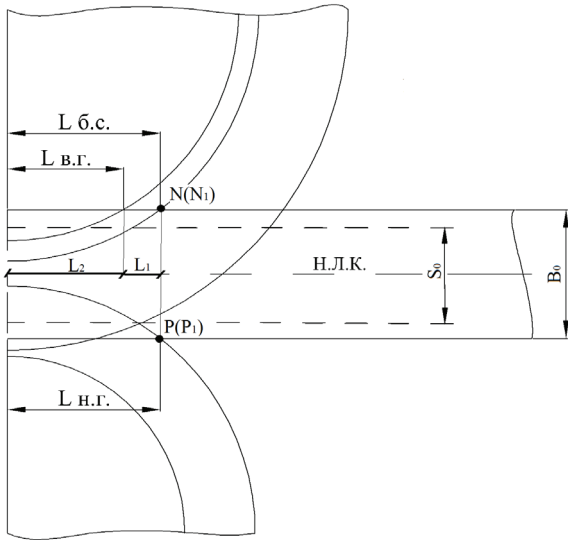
Первый фасонный черновой калибр рельсобалочного стана «800» с поступающей в него исходной заготовкой швеллера U-260
